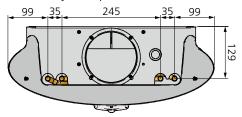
Dimensions ADRIATIC AWC Ellips, vue arrière du raccordement hydraulique
